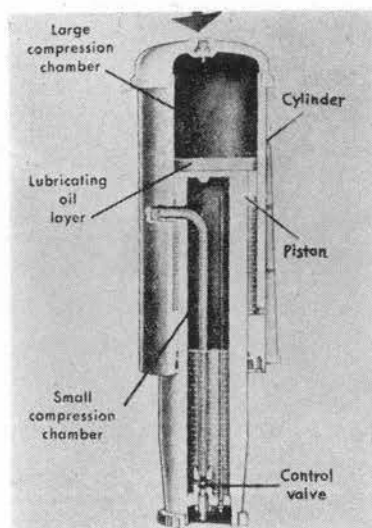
Le Tourneau-Westinghouse 社 Haulpak 用 Hydrair Suspension
